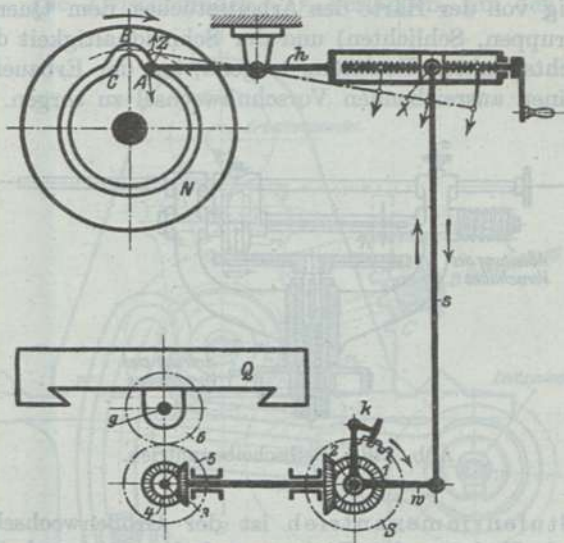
Plan der Steuerung einer Stoßmaschine.
